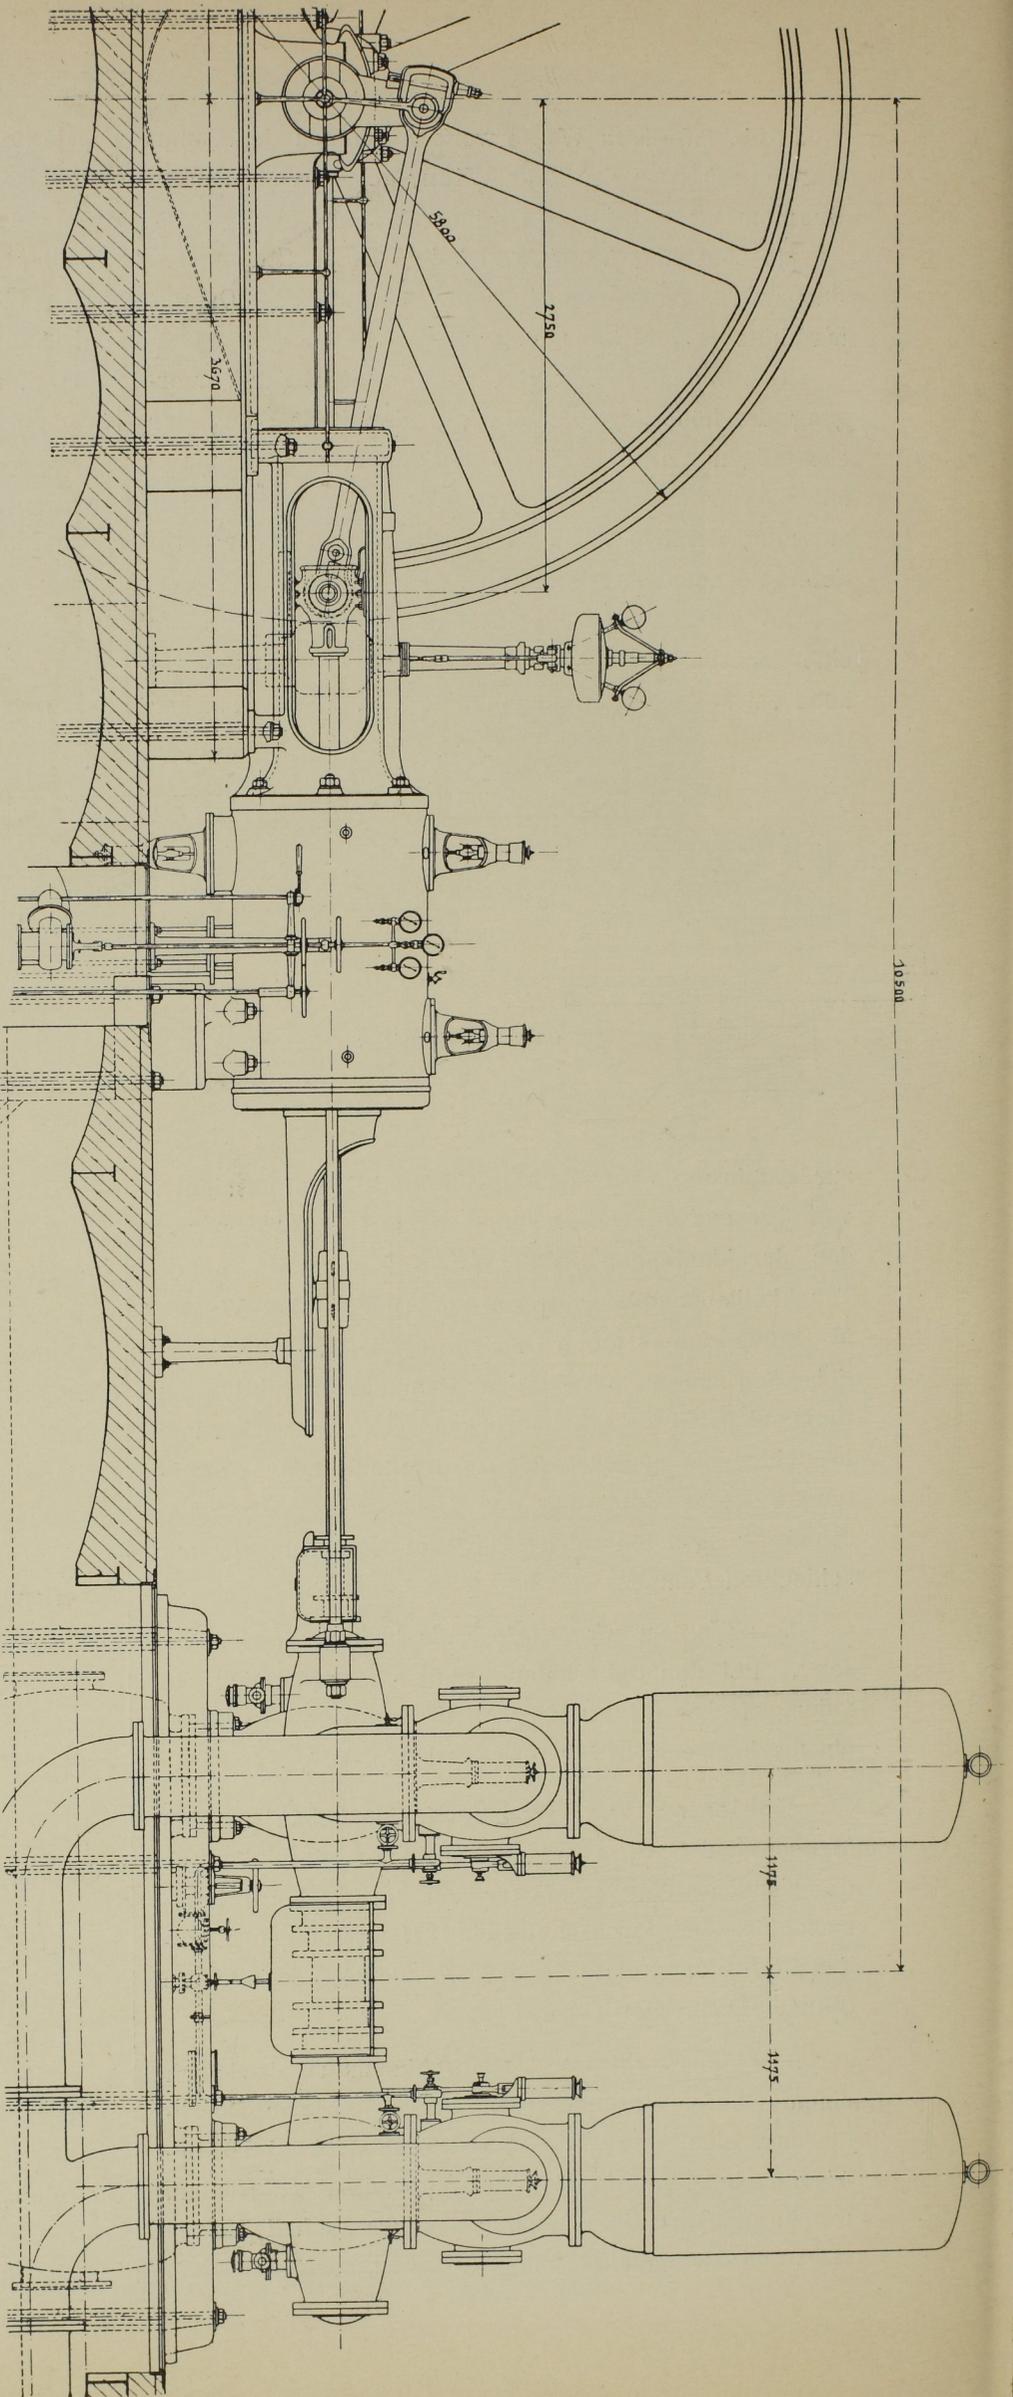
Seitensicht der Pumpmaschine. Massst. 1:40.
